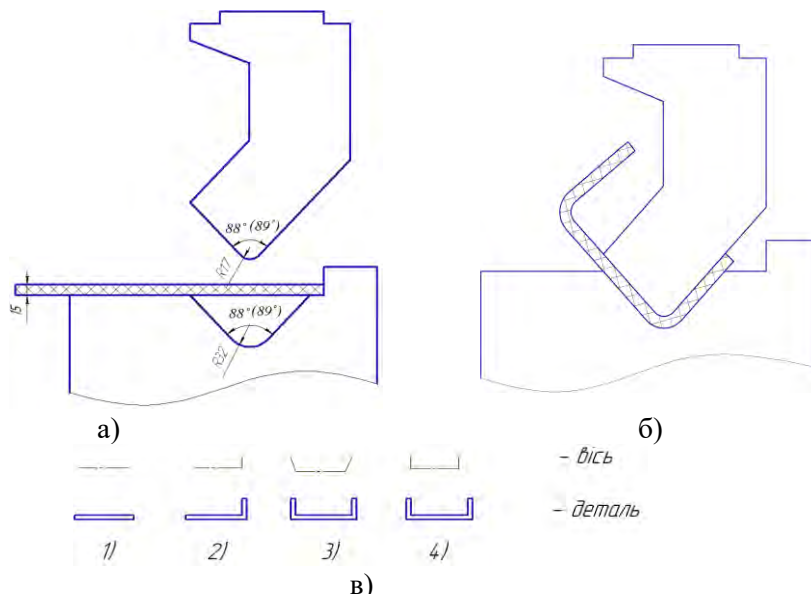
Поелементне гнуття деталі інструментом із плоскими контактними поверхнями:
